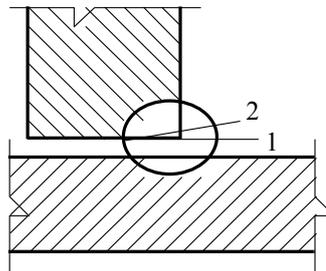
Схема расчетных сечений сварного соединения с угловым швом. 1 – сечение по металлу шва; 2 – сечение по металлу границы сплавления.
